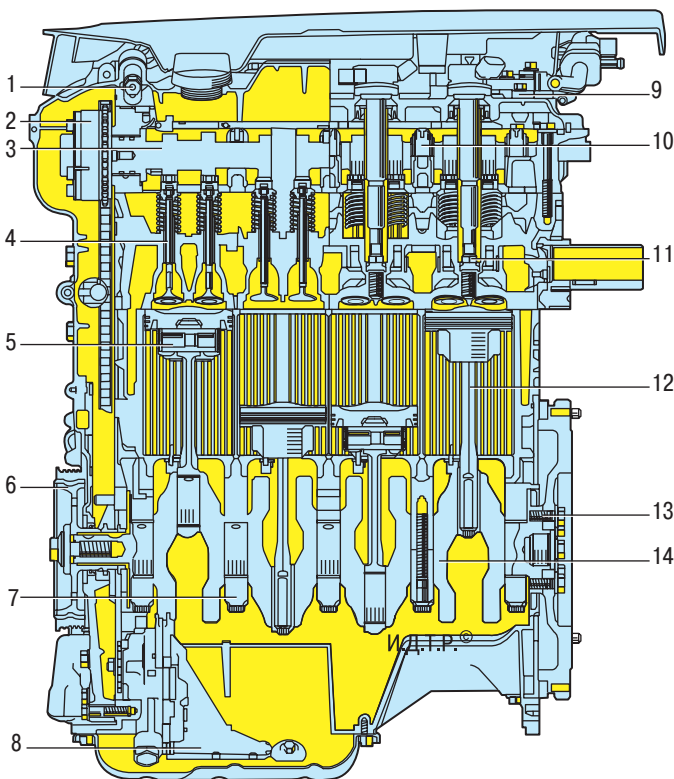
Двигатель 1ZR-FE (продольный разрез): 1 – гидравлический клапан изменения фаз газораспределения; 2 – контроллер системы VVT-i; 3 – распределительный вал; 4 – клапан; 5 – поршень; 6 – шкив привода вспомогательных агрегатов; 7 – крышка коренного подшипника; 8 – масляный насос; 9 – катушка зажигания; 10 – постель распределительного вала; 11 – свеча зажигания; 12 – шатун; 13 – задний сальник коленчатого вала; 14 – коленчатый вал
